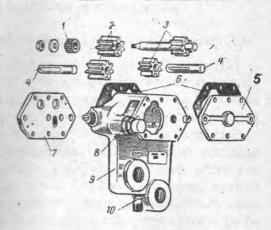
Детали масляного насоса МШ-8М: 1-шлицевая муфта; 2-шестерня откачивающей ступени; 3-шестерня нагнетающей ступени; 4-ось ведомой шестерни; 5-крышка корпуса насоса; 6-паронитовая прокладка; 7-опорный фланец; 8-редукционный клапан; 9-корпус;
